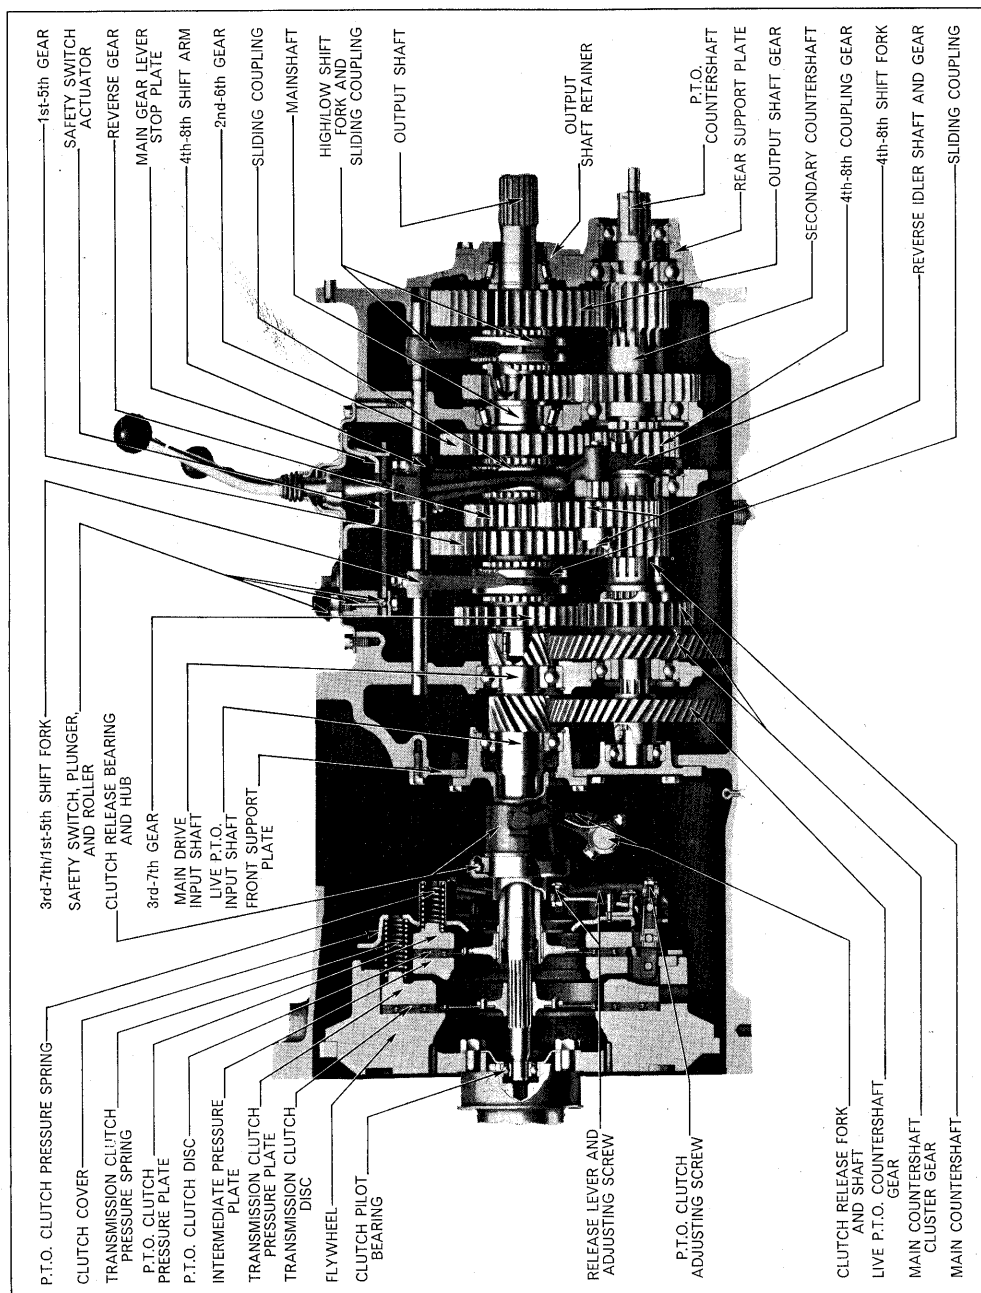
Gearkasse og reduktionsgearkasse (her med dobbeltkobling).
